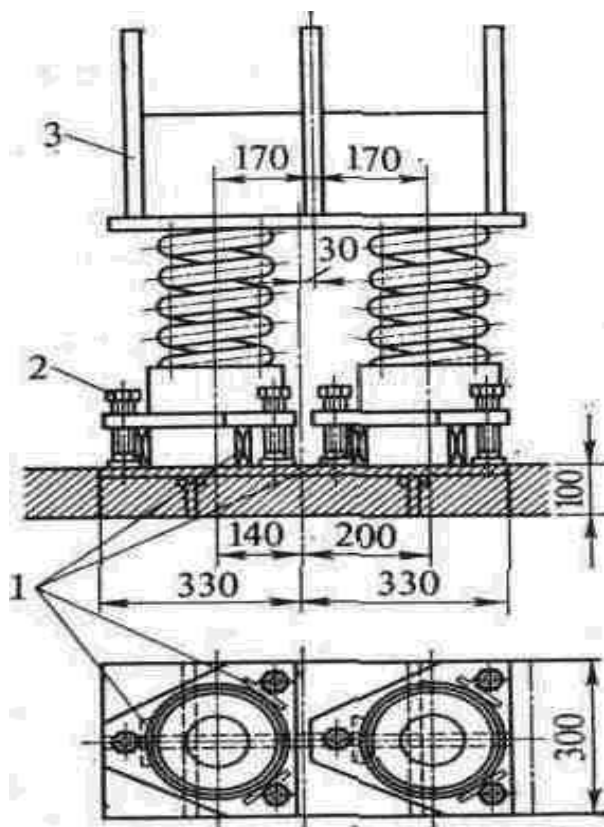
Пружинная опора конденсаторов при подвальном расположении: 1—установочные планки; 2—отжимные болты; 3—опорная лапа, приваренная к корпусу конденсатора.
